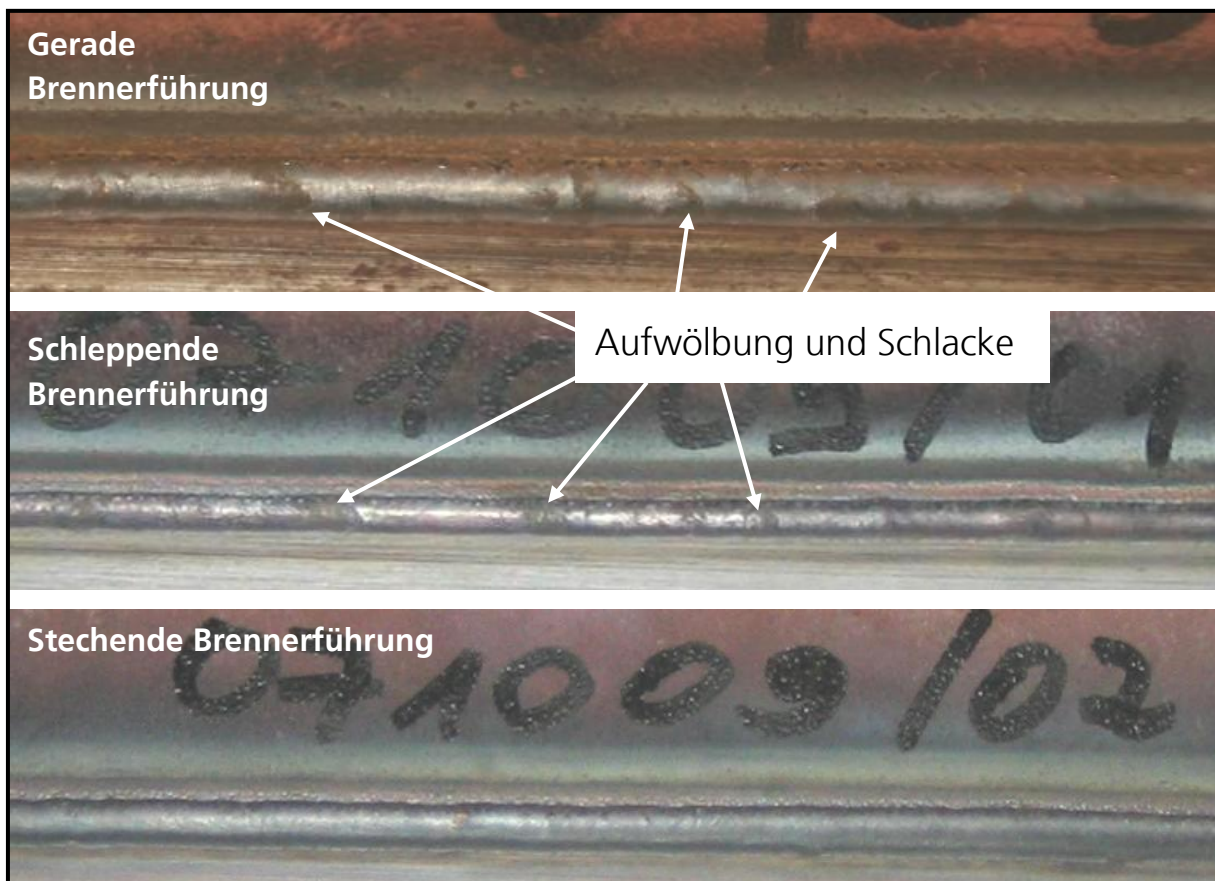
Bearbeitete Kanten (v. o.) mit gerader, schleppender, stechender Brennerführung
